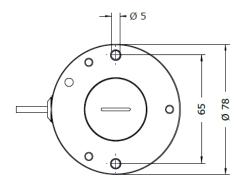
LP02/LP02-7mV/SR03 平面図(mm)
